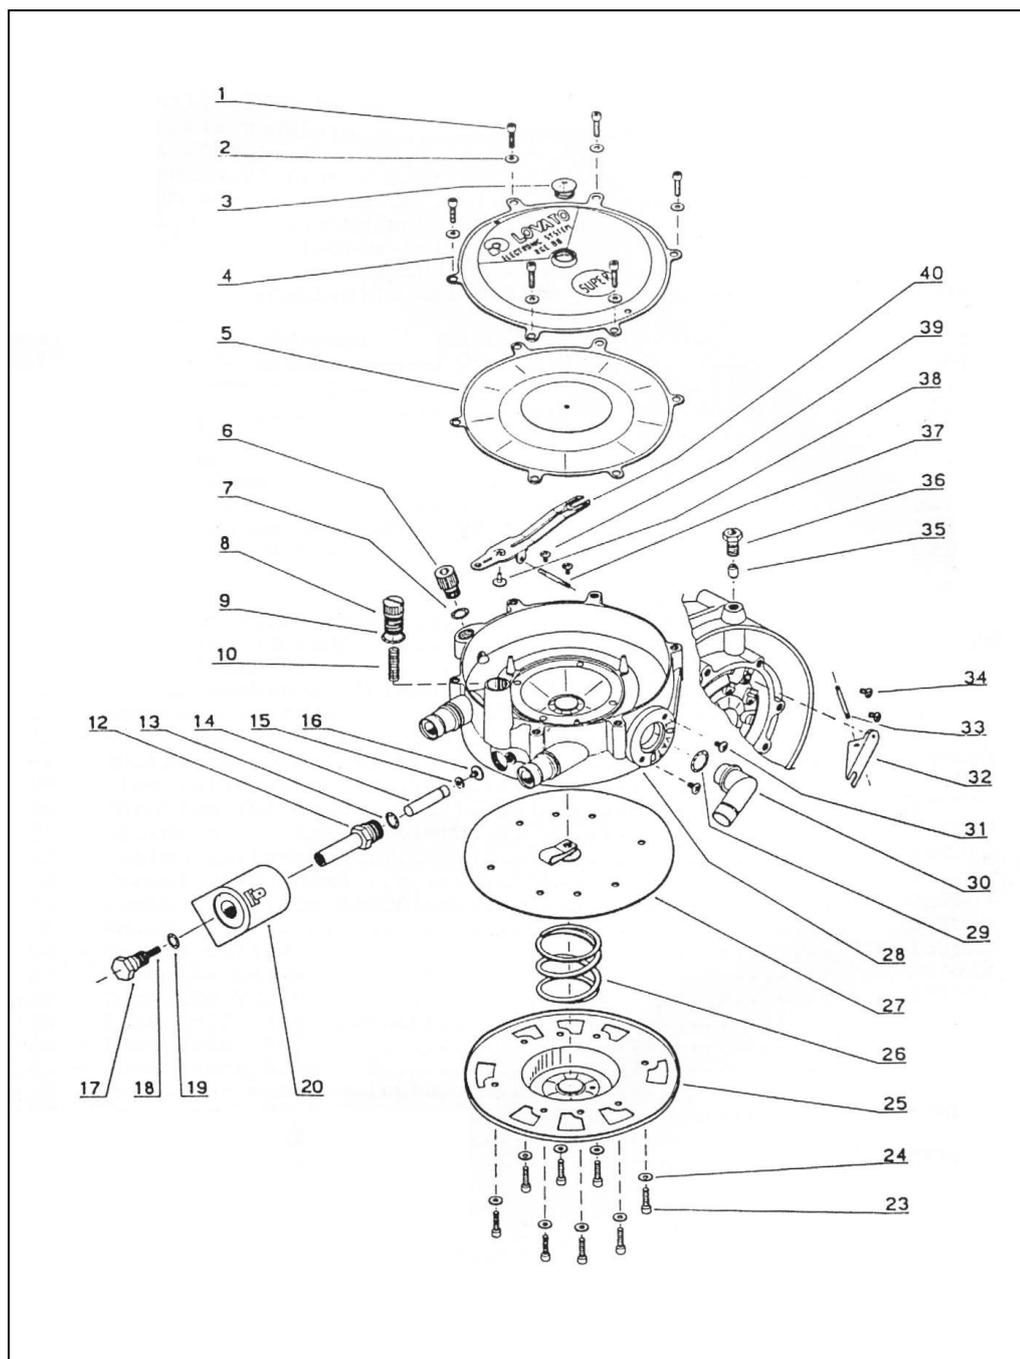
Esquema del despiece del Reductor-Vaporizador GLP Electrónico
